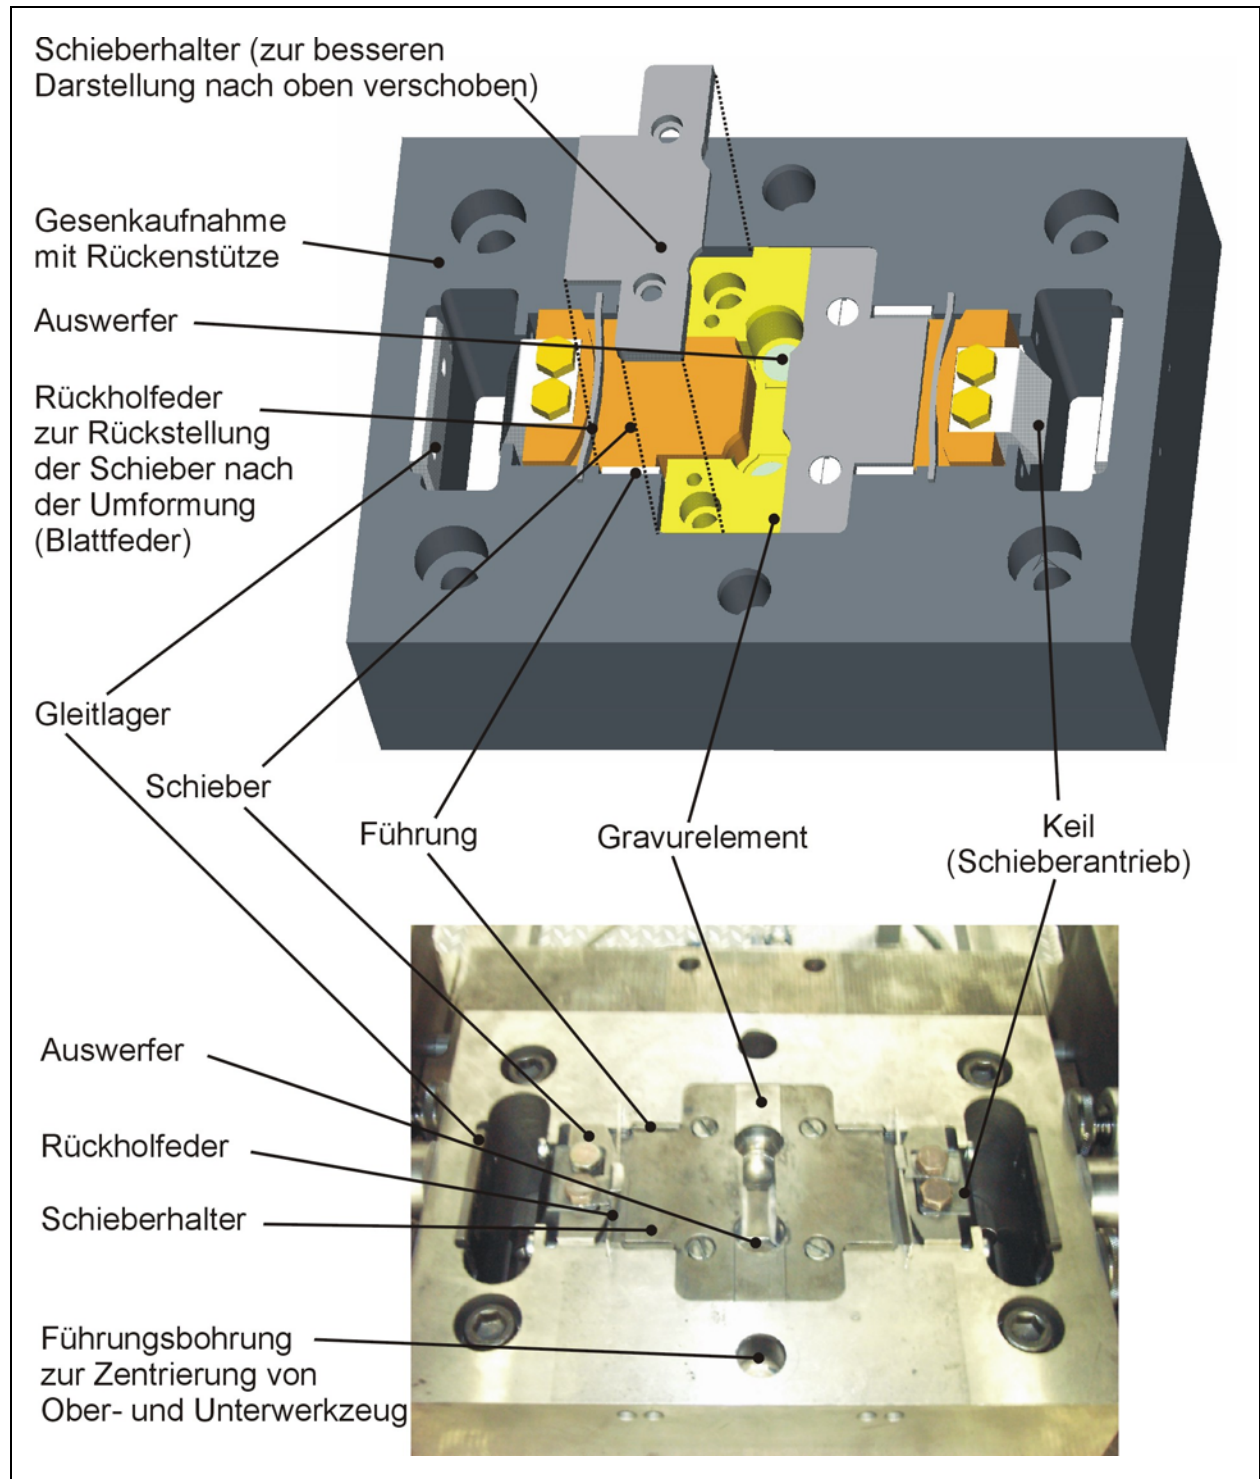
zeigt das Unterwerkzeug. Gravurelemente, Schieber, Gleitlager, Führung der Keilhalter und Auswerfer sind in einer Gesenkplatte angeordnet. Die Gesenkplatte ist wiederum auf der Grundplatte kraftschlüssig befestigt. Die Führungen der Schieber ermöglichen neben der Hauptfunktion *Führung* eine exakte Positionierung sowie die Einstellung der Spalte zwischen Schiebern und Gravurelementen. Die Schieber sind zweiteilig ausgeführt, so dass die Keilflächen zur Umleitung der Vertikalbewegung austauschbar sind. Rückholfedern zwischen Schiebern und Gesenkplatte ermöglichen ein Zurückschieben der Schieber in die Ausgangsposition nach Abschluss der Umformprozesse. Die Auswerfer erlauben eine leichte Entnahme des Werkstücks nach dem Öffnen des Gesenks.
